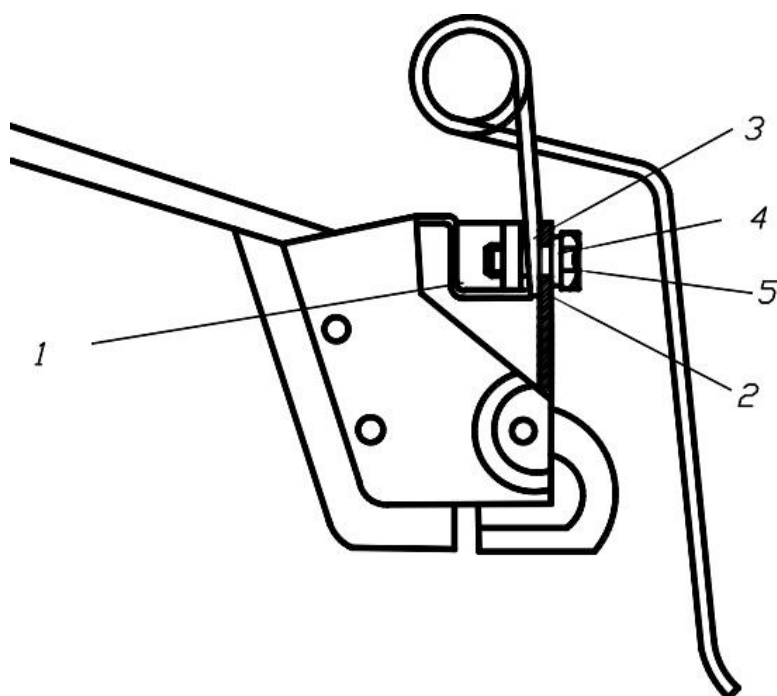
Схема установки пружинных загорточей анкерного сошника: 1 – карман сошника; 2 – пластина; 3 – загорточ; 4 – шайба; 5 – болт М8×20
